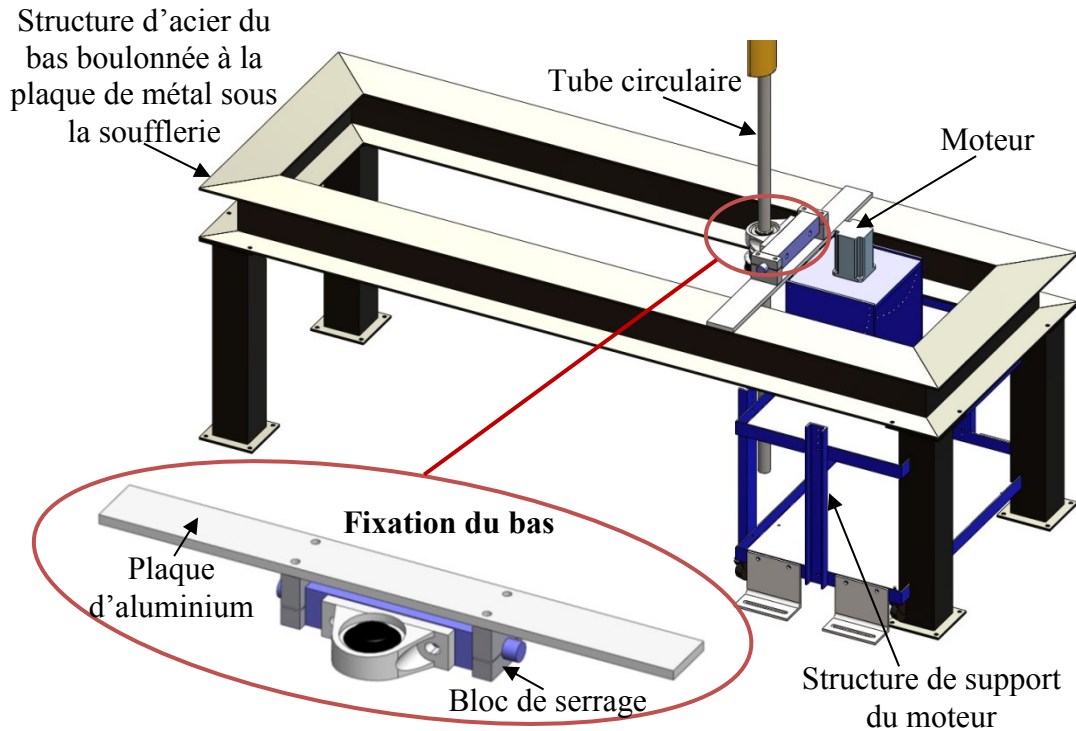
Montage sous la soufflerie permettant de fixer le bas du tube circulaire et structure de support du moteur
